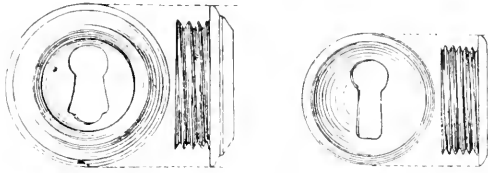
Schlüsselschilder aus Messing zum Einschrauben.
